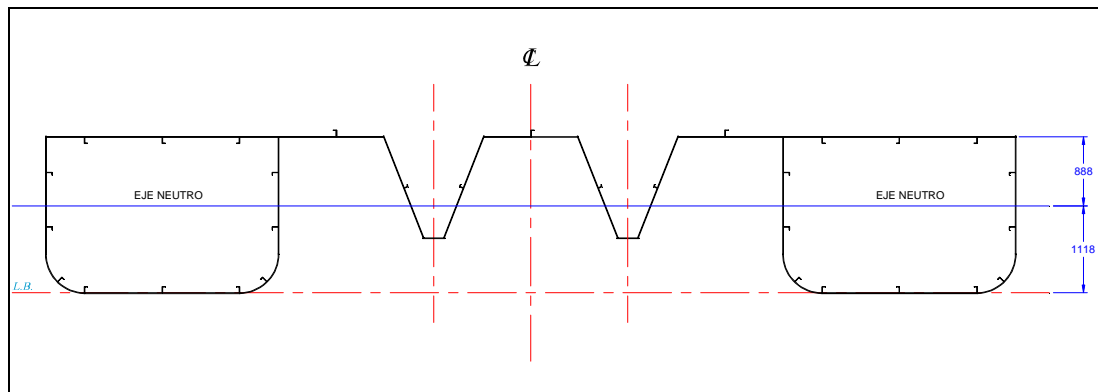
Vista de la sección transversal del empujador fluvial tipo catamarán
